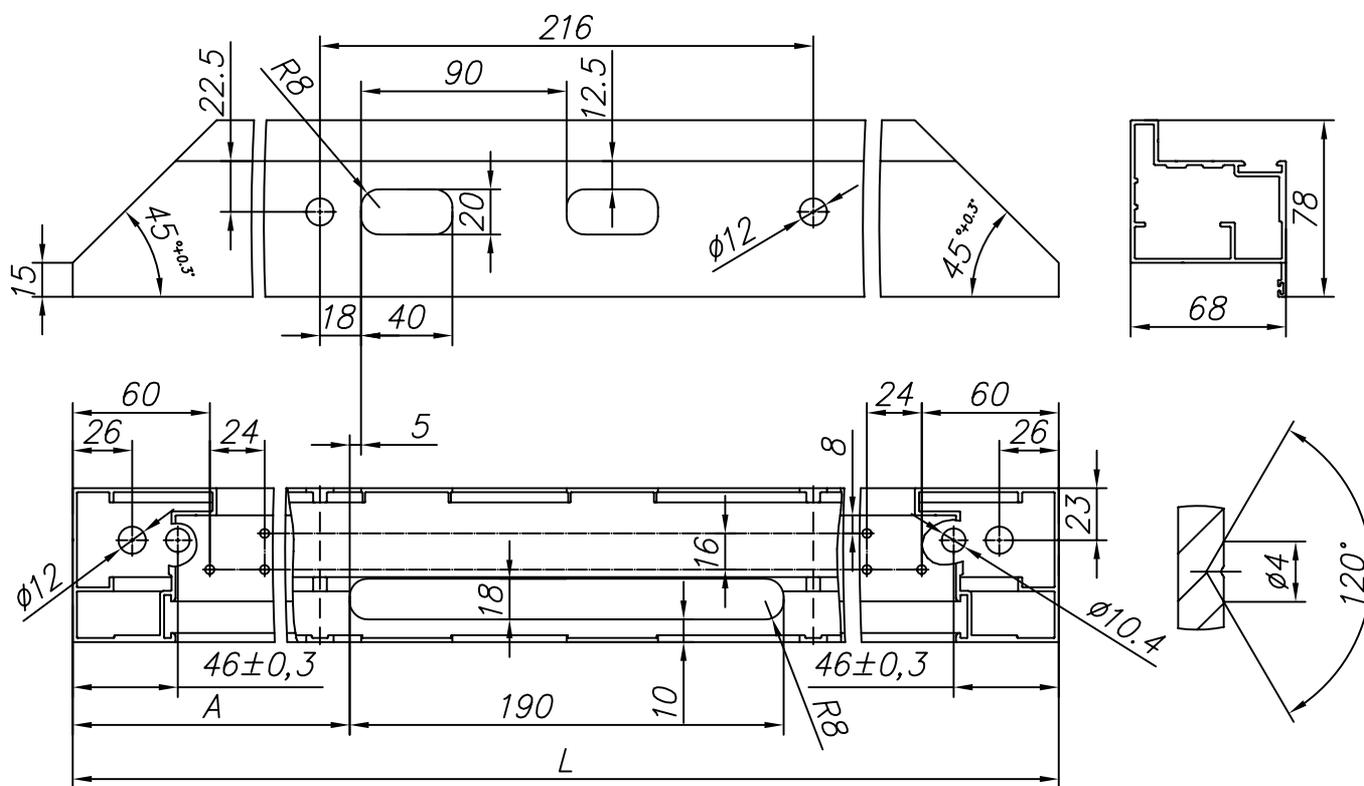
Изготовление стойки с пазом для замка из профиля FLGU.400.0110 (открывание внутрь, влево)
